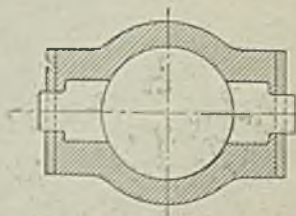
Ventilzylinder mit Außenkernen geformt.
